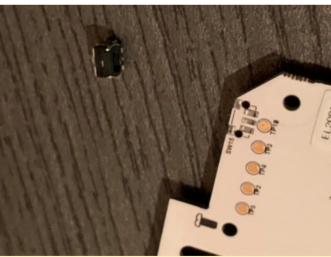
el componente SW15 también puede separarse de la placa durante el desmontaje
